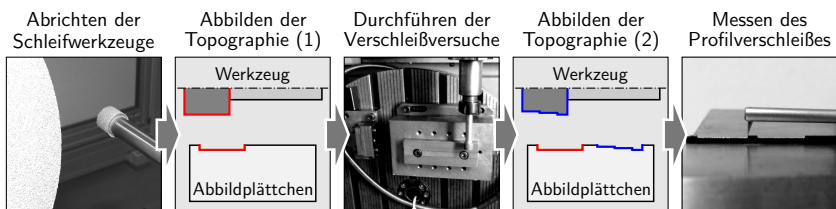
Prozesskette zur Identifikation des makroskopischen Werkzeugverschleißes beim Schleifen von Hartstoffschichten.
